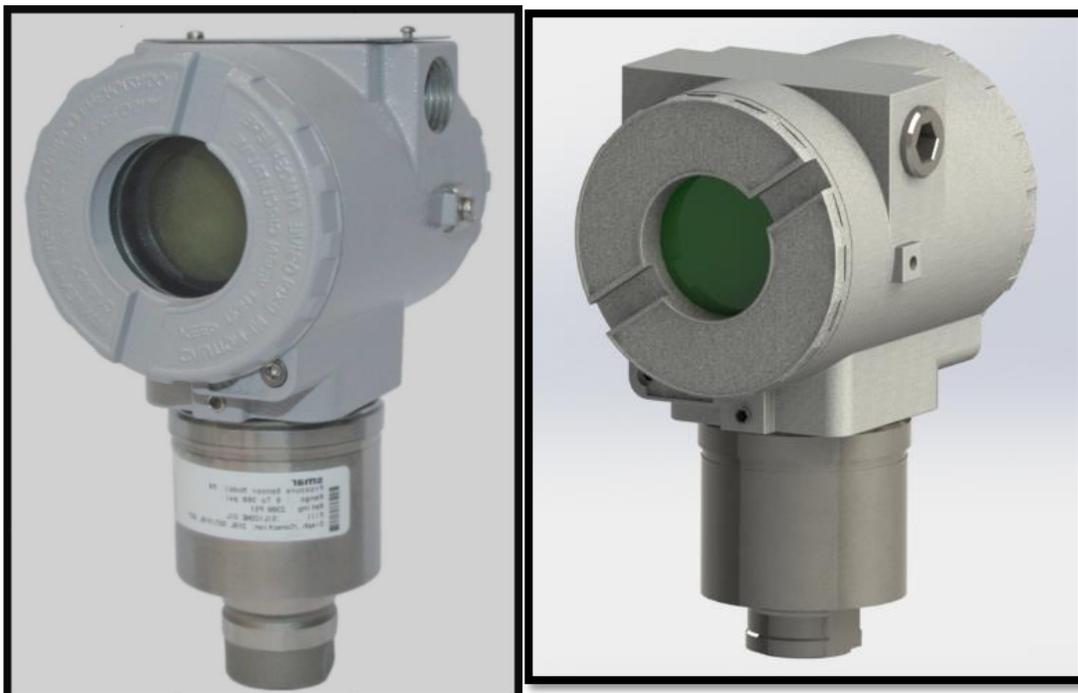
Imagen izquierda, transmisor Smar LD291 [37],
